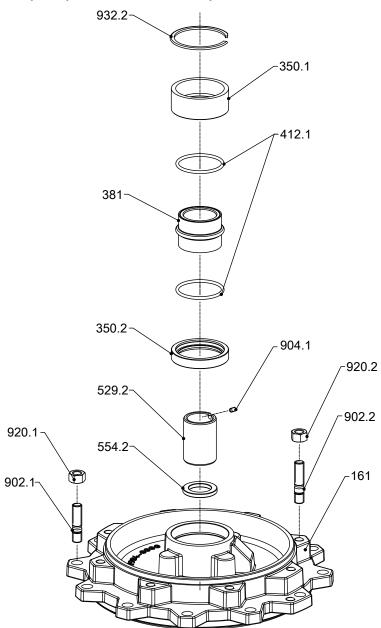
Монтаж крышки корпуса для подшипниковой опоры типоразмера VCS 50 и VCS 80
